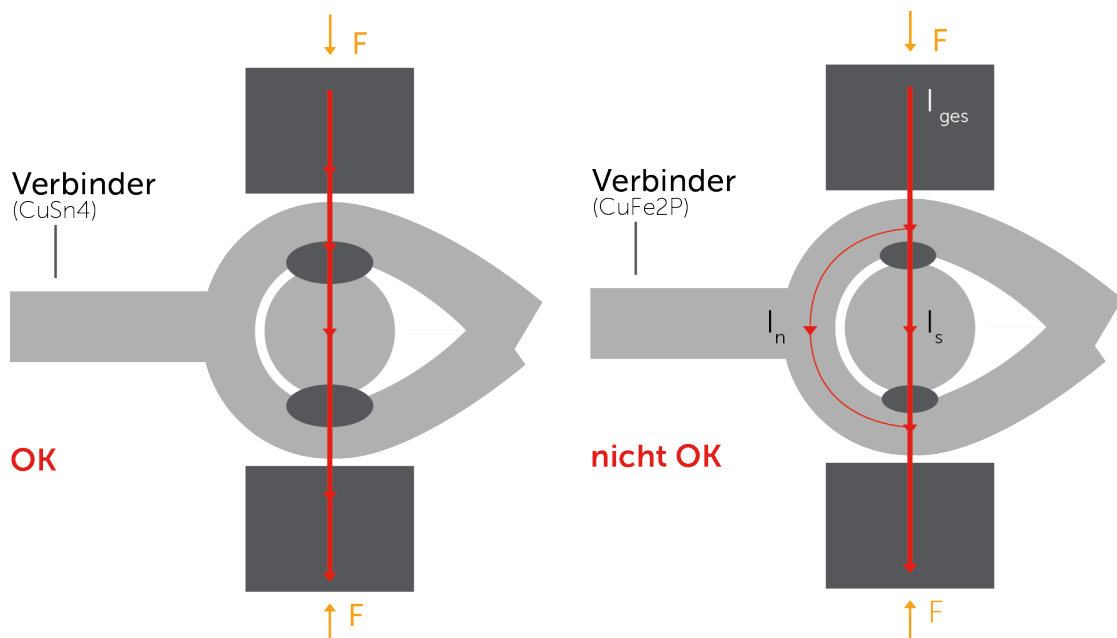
Nebenschluss aufgrund nicht an den Werkstoff angepasster Bauteilgeometrie (rechts) – bei der abgebildeten Bauteilgeometrie ist die Schweißung mit einem Verbinder aus Wieland-B14 (CuSn4) realisierbar, mit einem Verbinder aus Wieland-K65 (CuFe2P) jedoch nicht, da dieser Werkstoff eine höhere elektrische Leitfähigkeit besitzt und den Schweißstrom somit an der Fügestelle vorbeileitet. Schweißparameter, Werkstoff und Bauteildesign sind im rechten Bild folglich unzureichend aufeinander abgestimmt.
